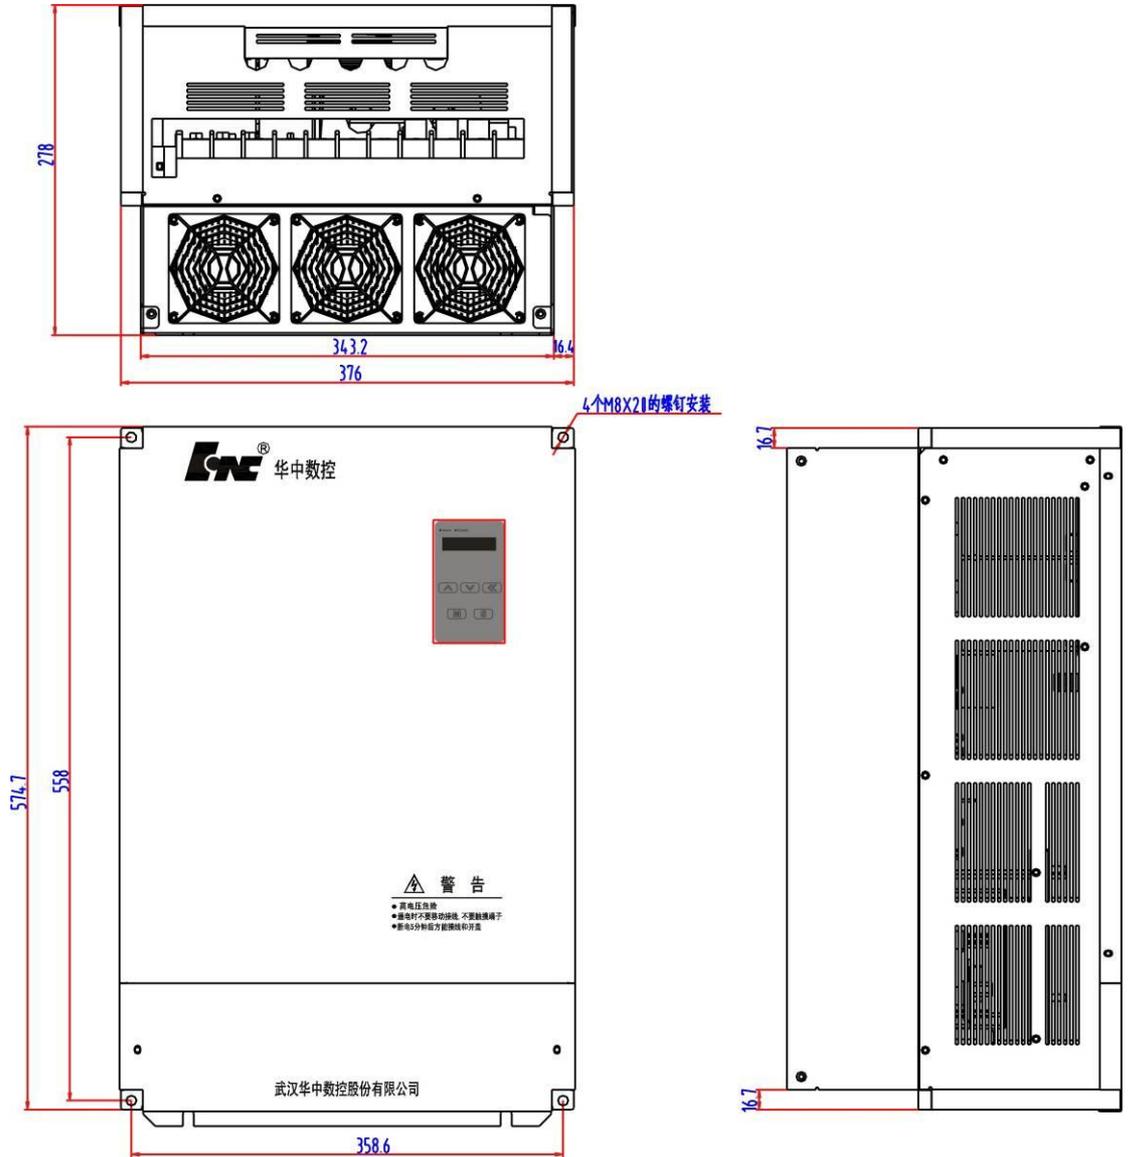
HSV-180AD-200, 300, 450 伺服驱动单元外形尺寸 (未带辅助安装装置 单位: mm)
